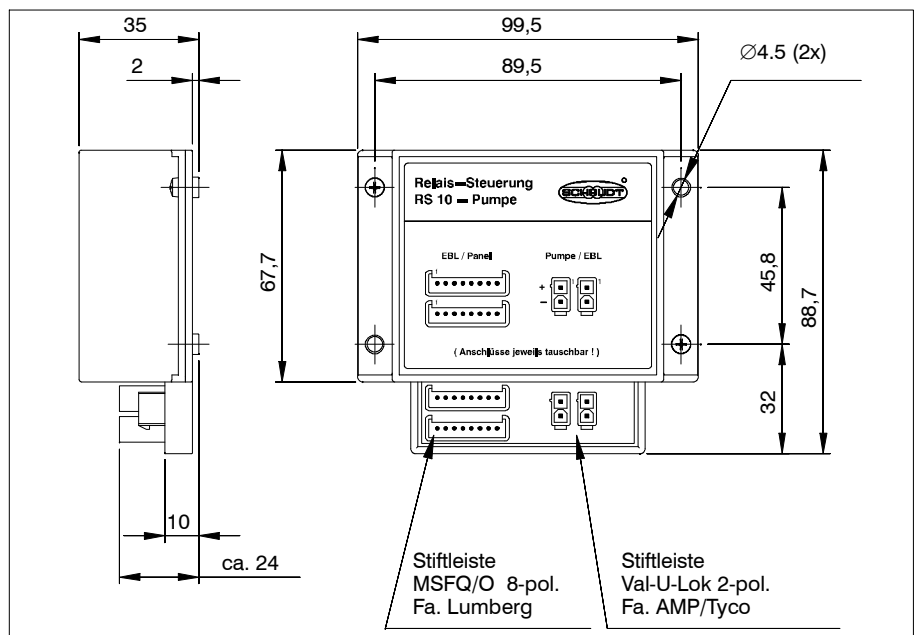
Maßbild Relais-Steuerung RS 10 (Abmessungen in mm)
